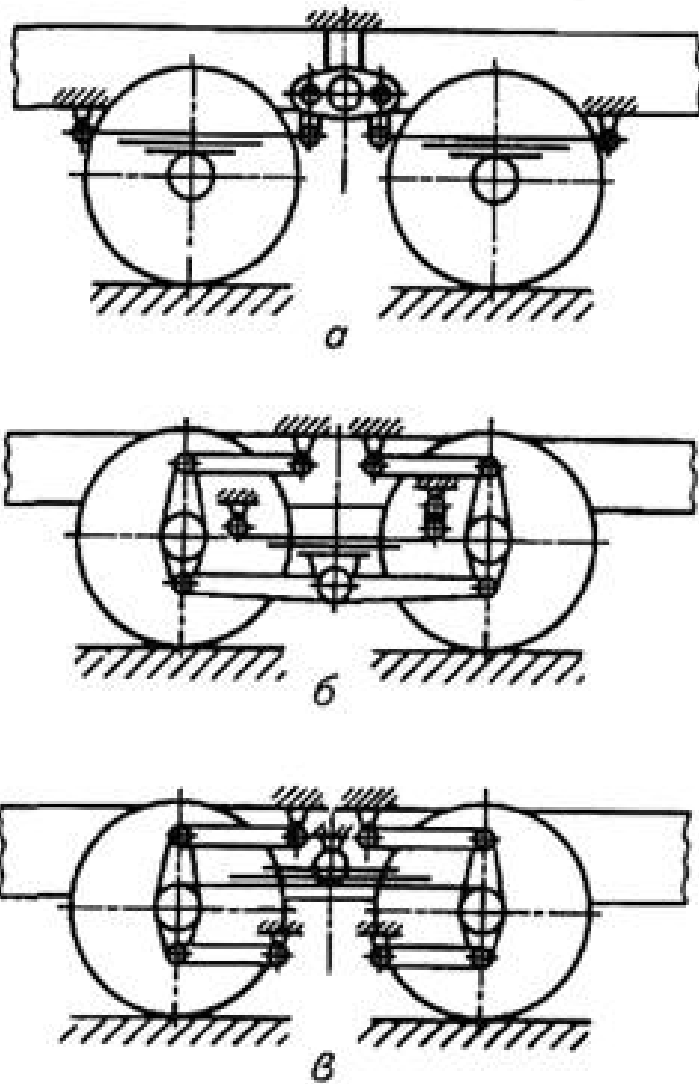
Схема балансирных подвесок: а - четырехрессорная с балансиром; б - двухрессорная с жесткой балансирной балкой; в - с балансирными рессорами и реактивными штангами
